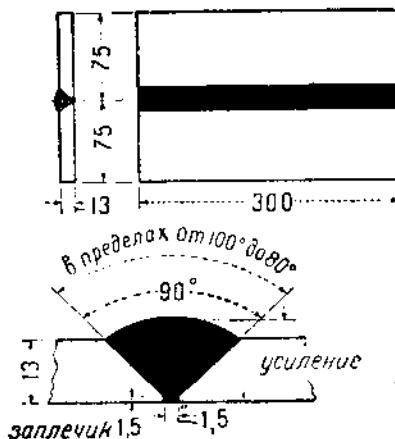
Сварка встык односторонним V-образным швом.
